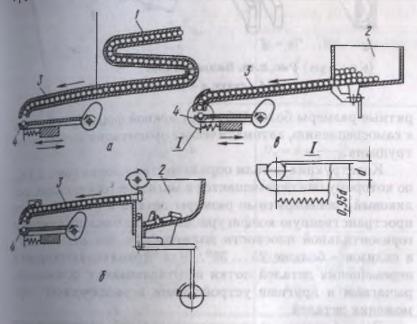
Схемы загрузочных устройств: 1 - магазин; 2 - бункер; 3 - накопитель; 4 - питатель
